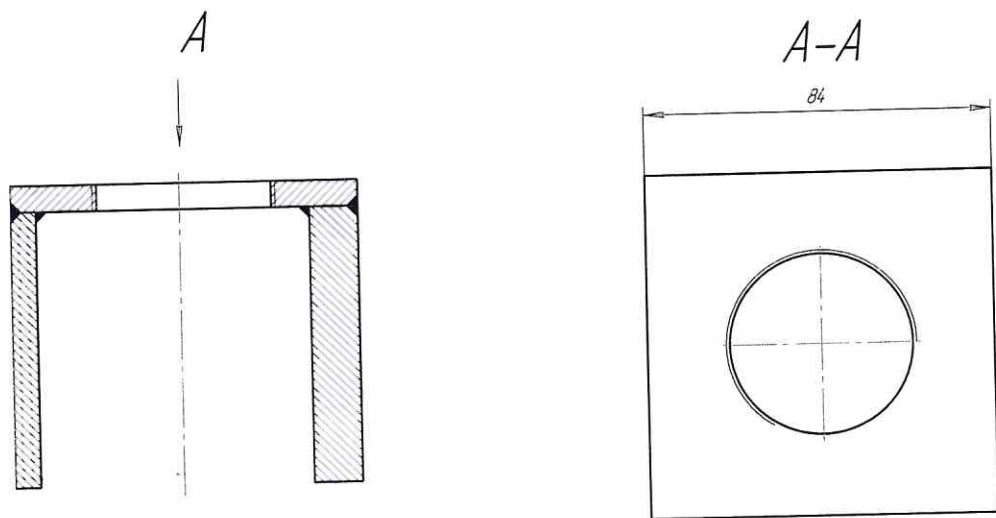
Сварное соединение корпуса двигателя
